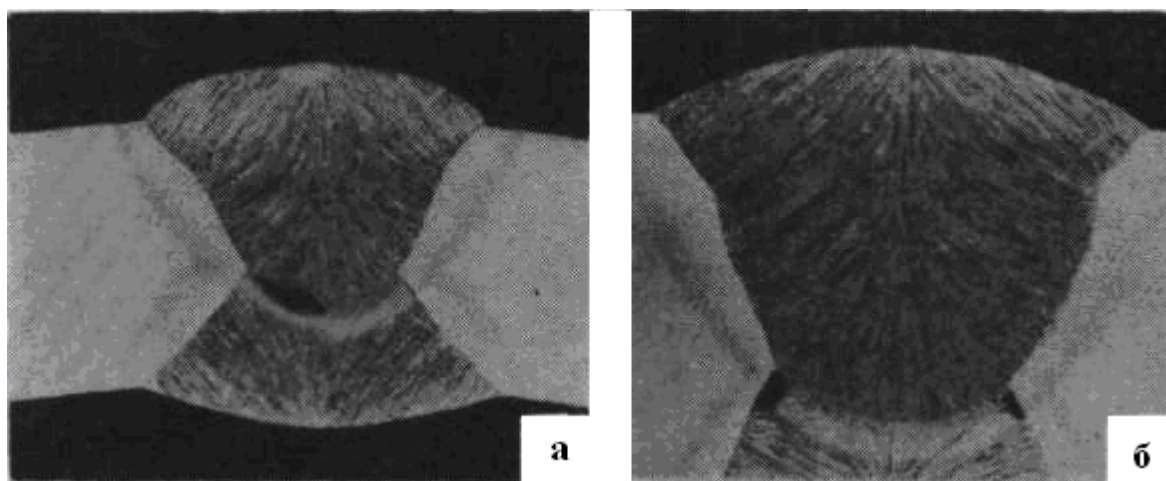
Шлаковые включения в сварном шве: а – в сечении; б – по кромке.
